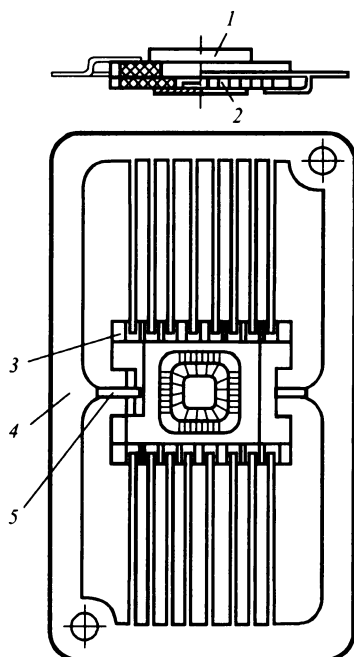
Плоский металлокерамический корпус с планарными выводами:
